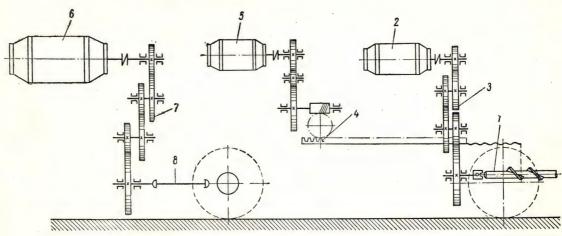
Кинематическая схема бурового станка «Сибиряк»
